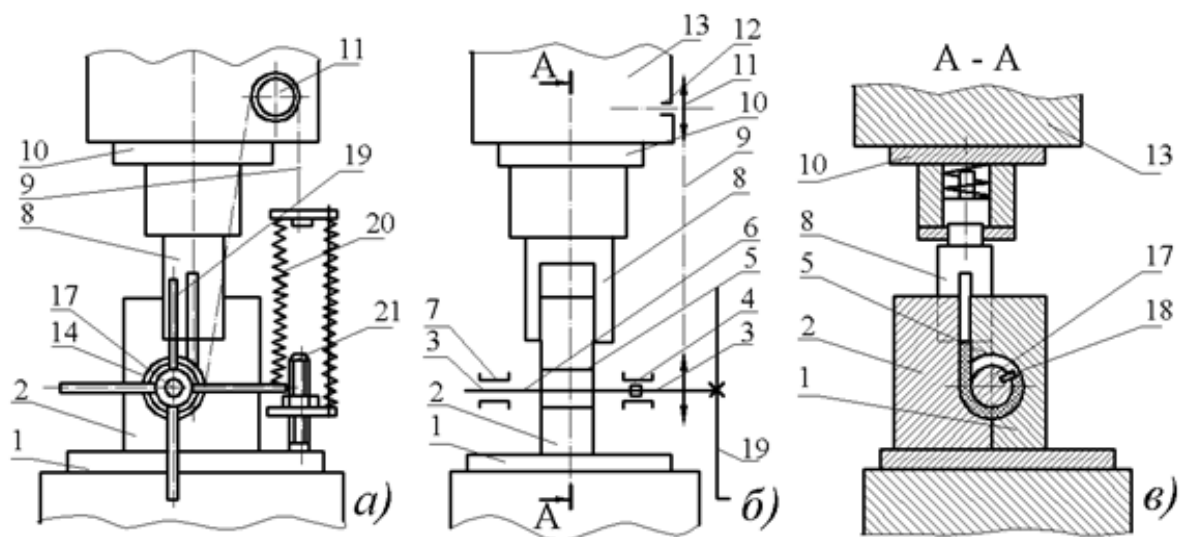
Схематичне зображення пристрою для виготовлення втулок із листових заготовок
